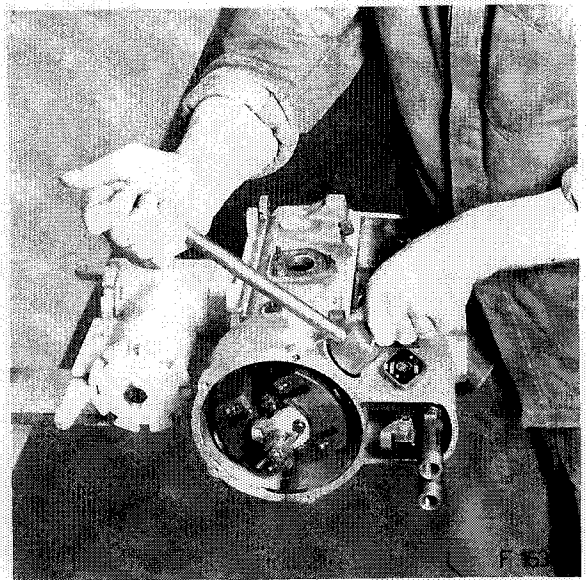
Lösen der Verschlusschraube im Reglergehäuse
